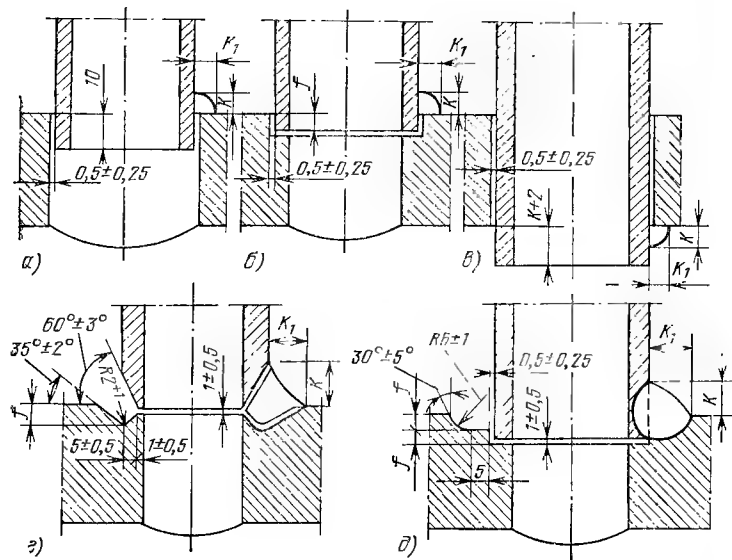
Конструкции сварных соединений труб с коллекторами и барабанами.
